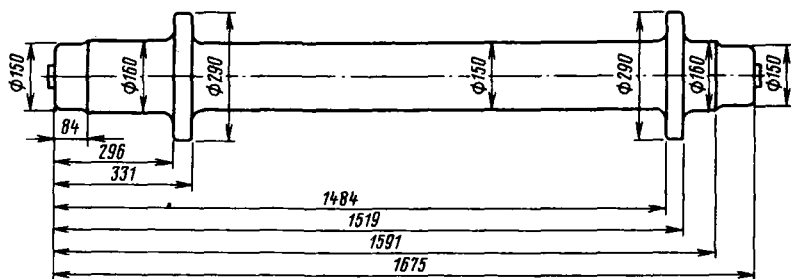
Главный приводной вал эскалатора ЭТ-5
